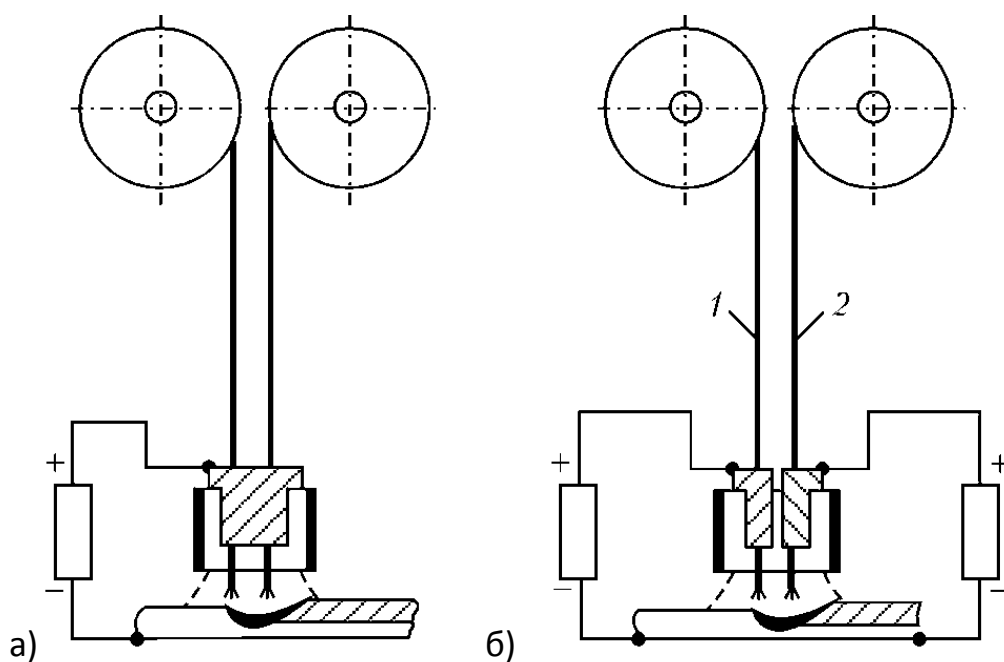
Известные схемы сварки: а) двухэлектродная; б) двухдуговая
